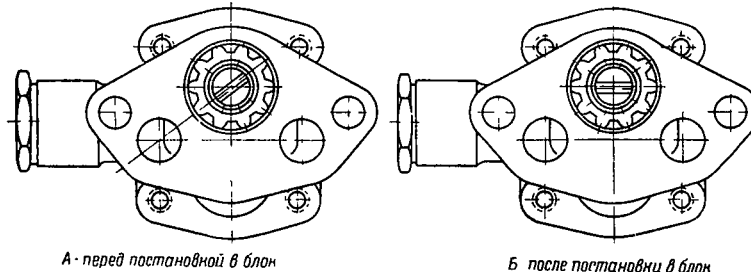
Положение паза на торце валика масляного насоса (вид на валик сверху)
